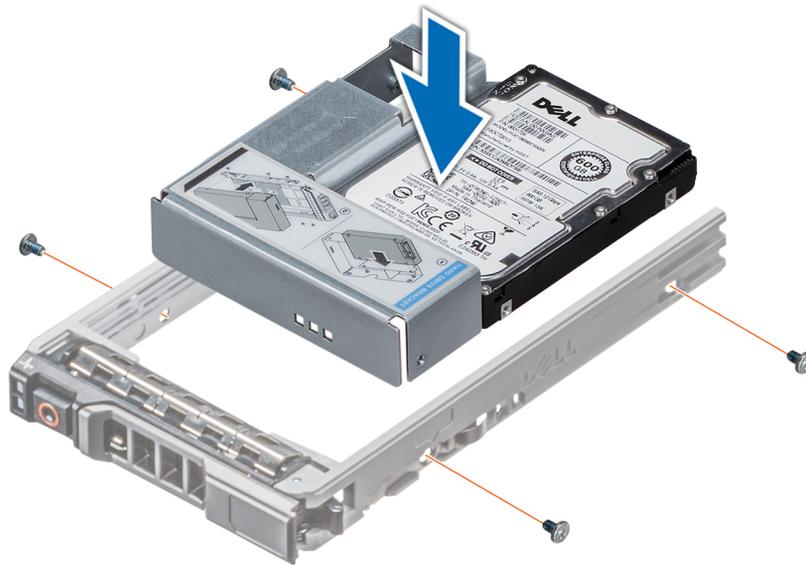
Installieren eines 3,5-Zoll-Laufwerkadapters im 3,5-Zoll-Laufwerkträger
